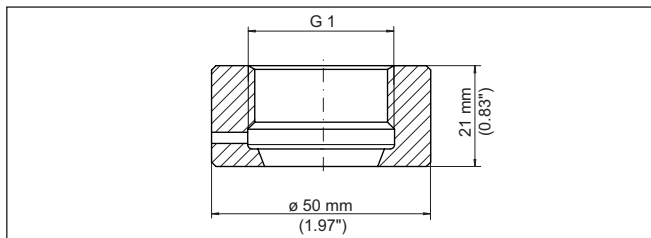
Dimensions raccord à souder direct G1 (ISO 228-1) - joint conique
